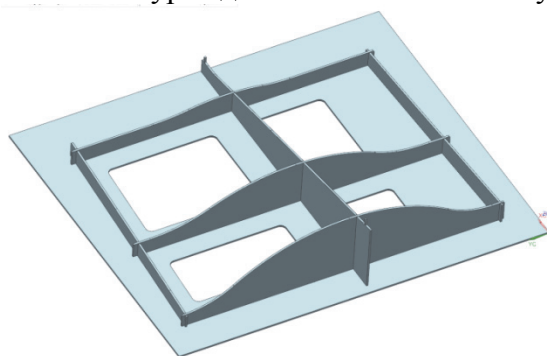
Приспособление для гидроабразивной резки детали «Решетка»
